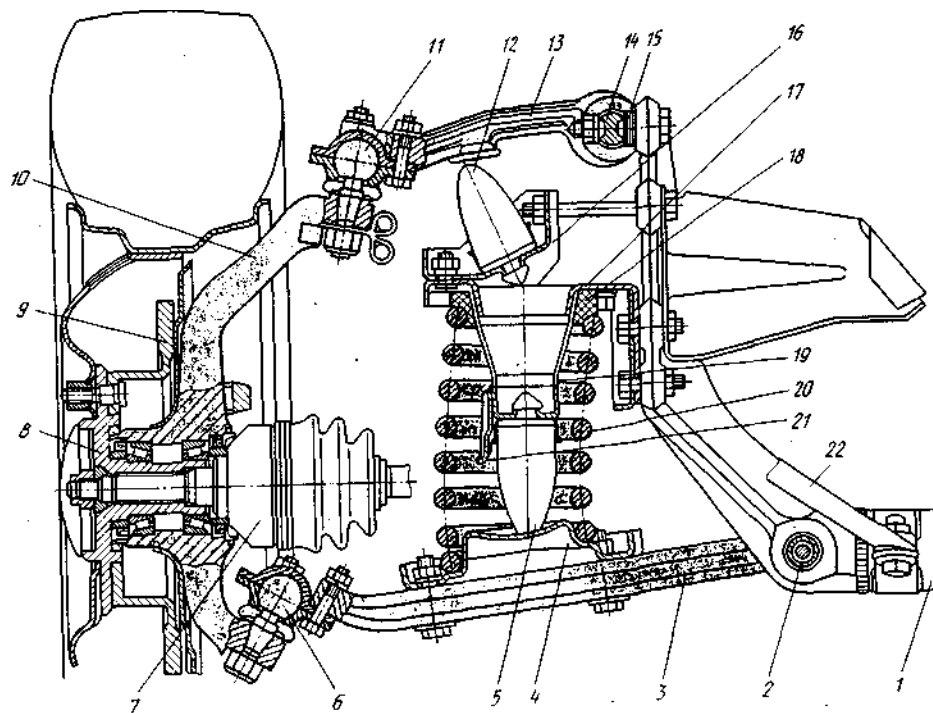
Передняя подвеска легкового автомобиля ВАЗ-2121 «Нива»: 1 — поперечина; 2 — ось нижнего рычага; 3 — нижний рычаг; 4 и 17 — соответственно нижняя и верхняя опорные чашки пружины; 5 — буфер сжатия; 6 и 11 — соответственно нижний и верхний шаровые шарниры; 7 — наружный шарнир привода переднего колеса; 8 — ступица; 9 — тормозной диск; 10 — поворотный кулак; 12 — буфер отдачи; 13 — верхний рычаг; 14 — ось верхнего рычага; 15 — регулировочные прокладки; 16 — кронштейн; 18 — виброшумоизолирующая прокладка; 19 — опора; 20 — пружина; 21 — упор; 22 — растяжка
